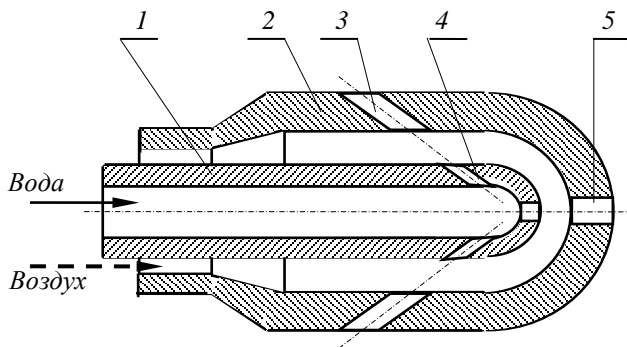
Схема головки для водно-воздушной промывки дрен: 1 – внутренний корпус; 2 – наружный корпус; 3 – задние отверстия; 4 – сопла; 5 – переднее отверстие
